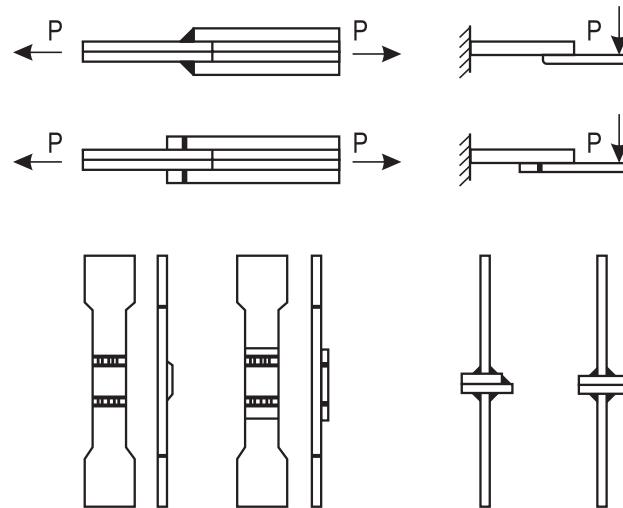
Образцы для оценки служебных свойств нахлесточных сварных соединений с различным конструктивным оформлением:
